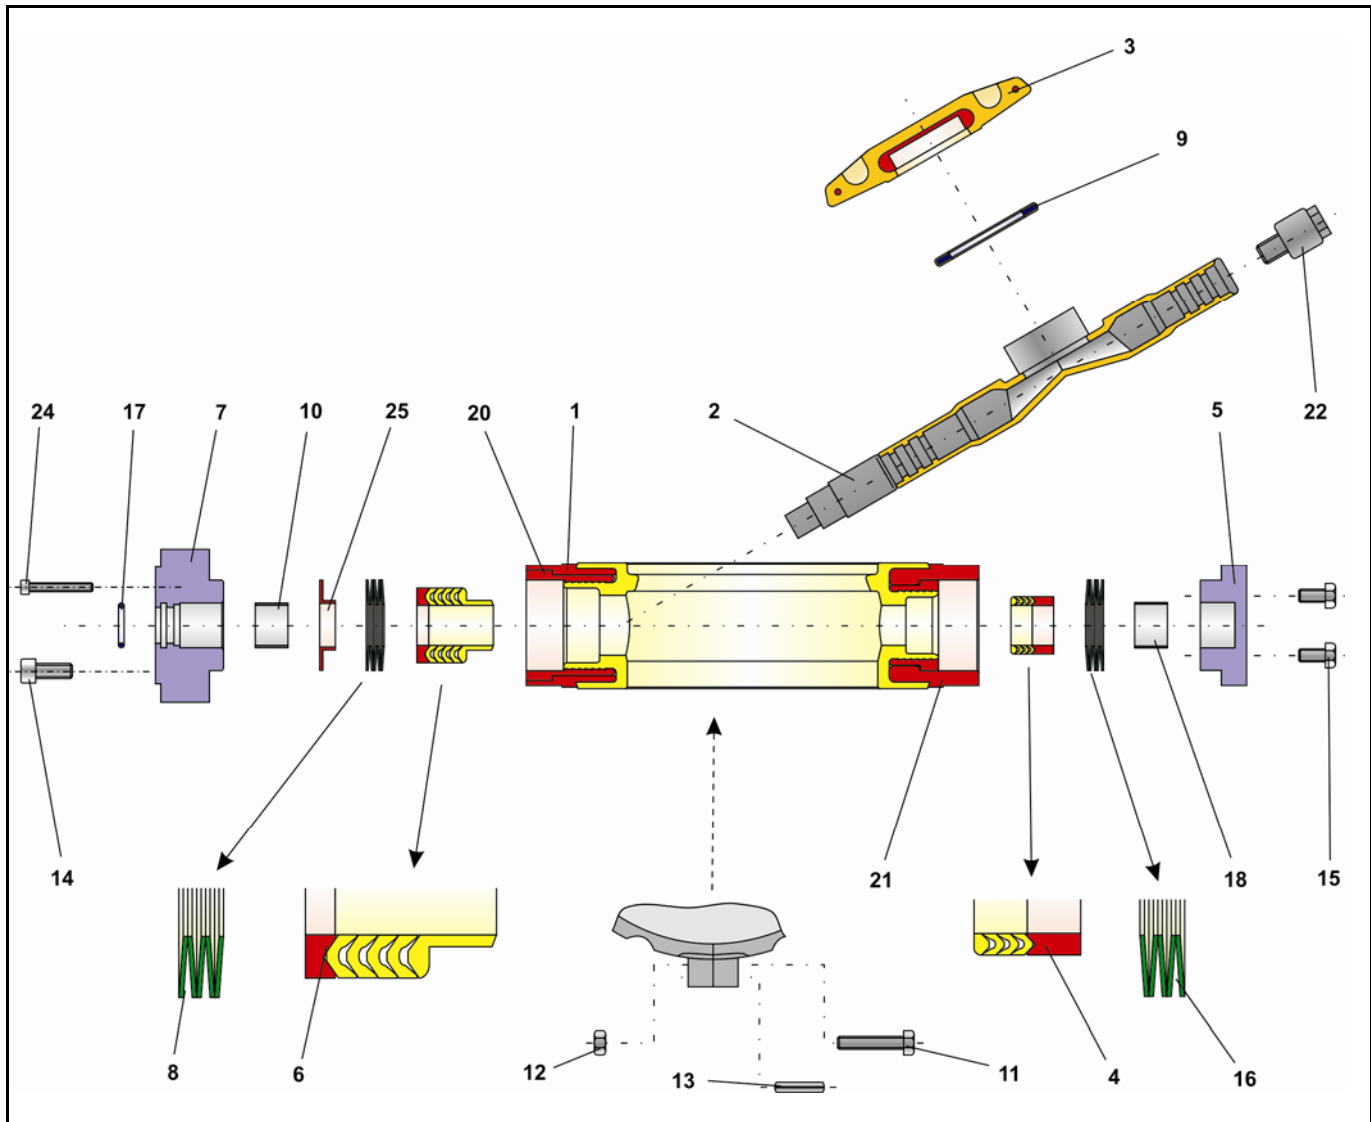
Детальная схема заслонки с регулируемой заглушкой BR 10a
